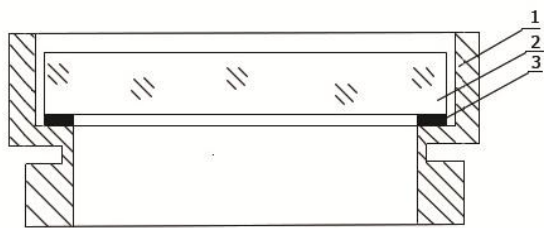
Стандартна конструкція паяного вікна в металевий корпус: 1 — чашка металевого корпусу; 2 — вікно; 3 — припій.
